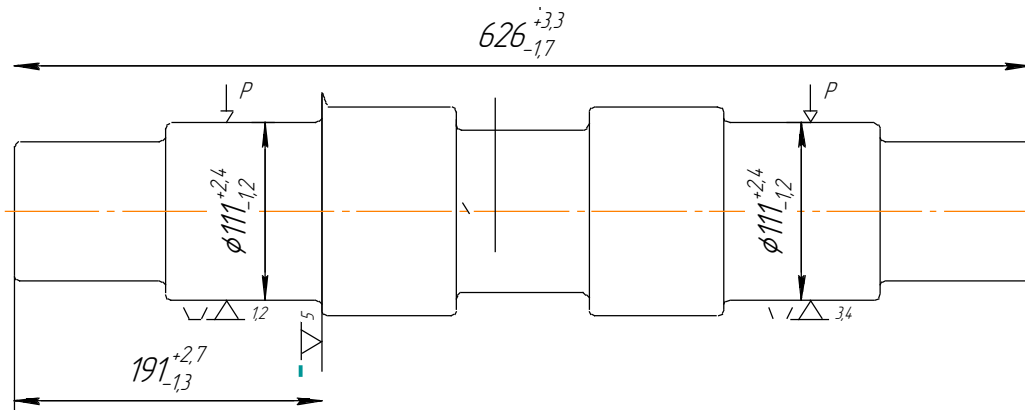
Схема базування вала-шестерні на фрезерно-центрувальній операції 030
